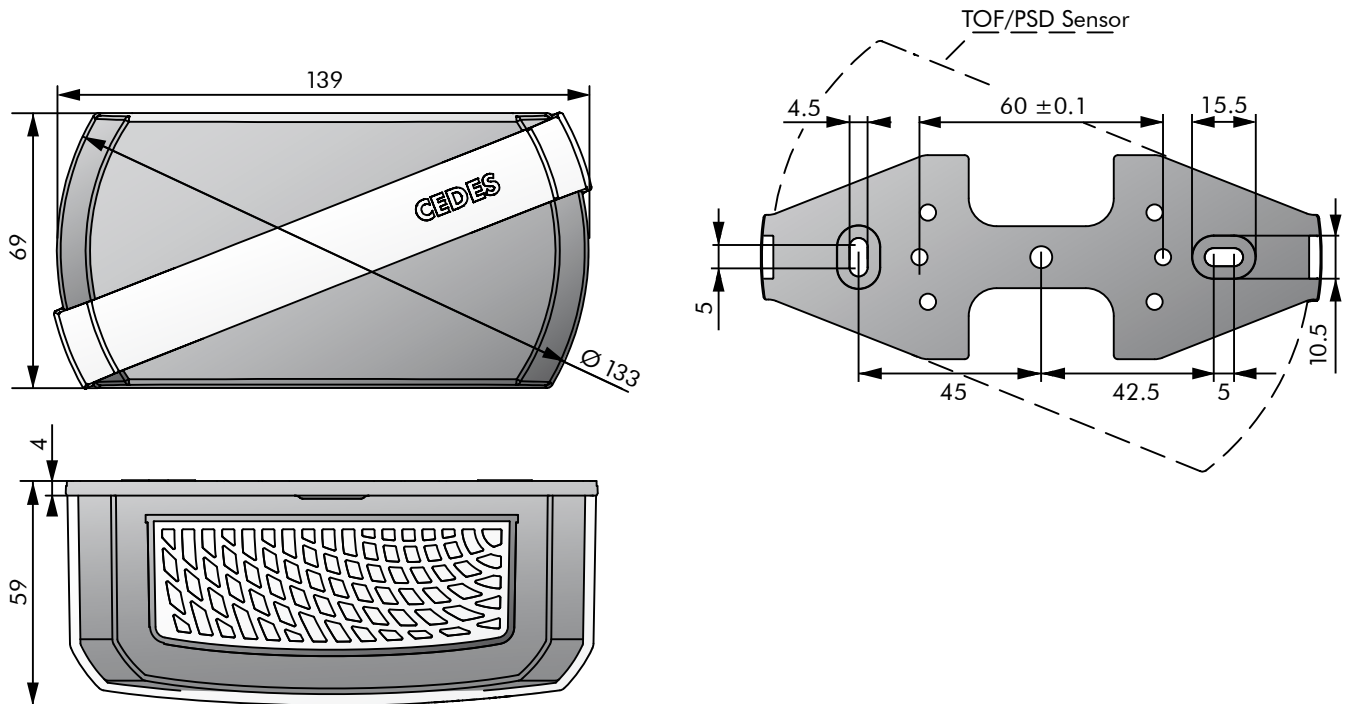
Abmessungen TOF/PSD (alle Masse in mm)
